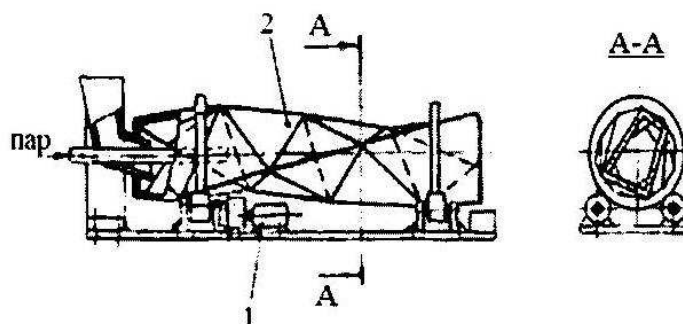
Схема предлагаемой конструкции установки на базе релятивного винтового барабана РЦ 5.1. а
